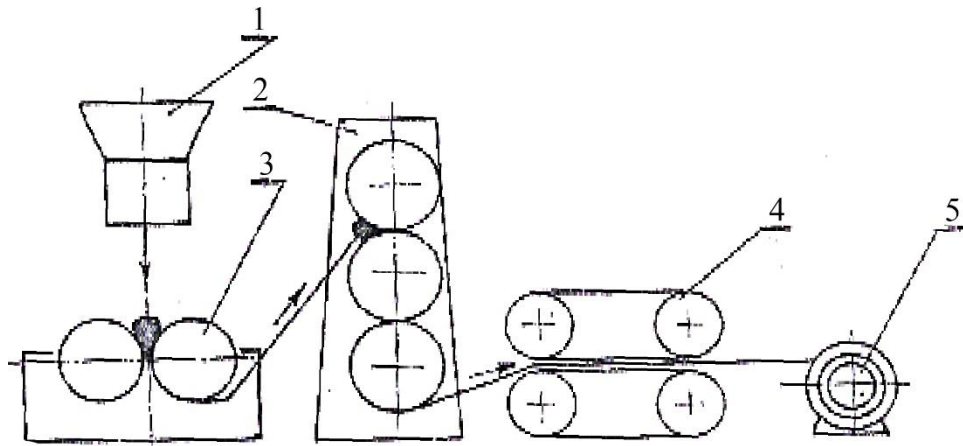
Схема переробки відходів ПВХ методом каландрування: 1 - бункер для суміші відходів; 2 - каландр; 3 - змішувальні вальці; 4 - притискний пристрій; 5 - намотувальний пристрій.
